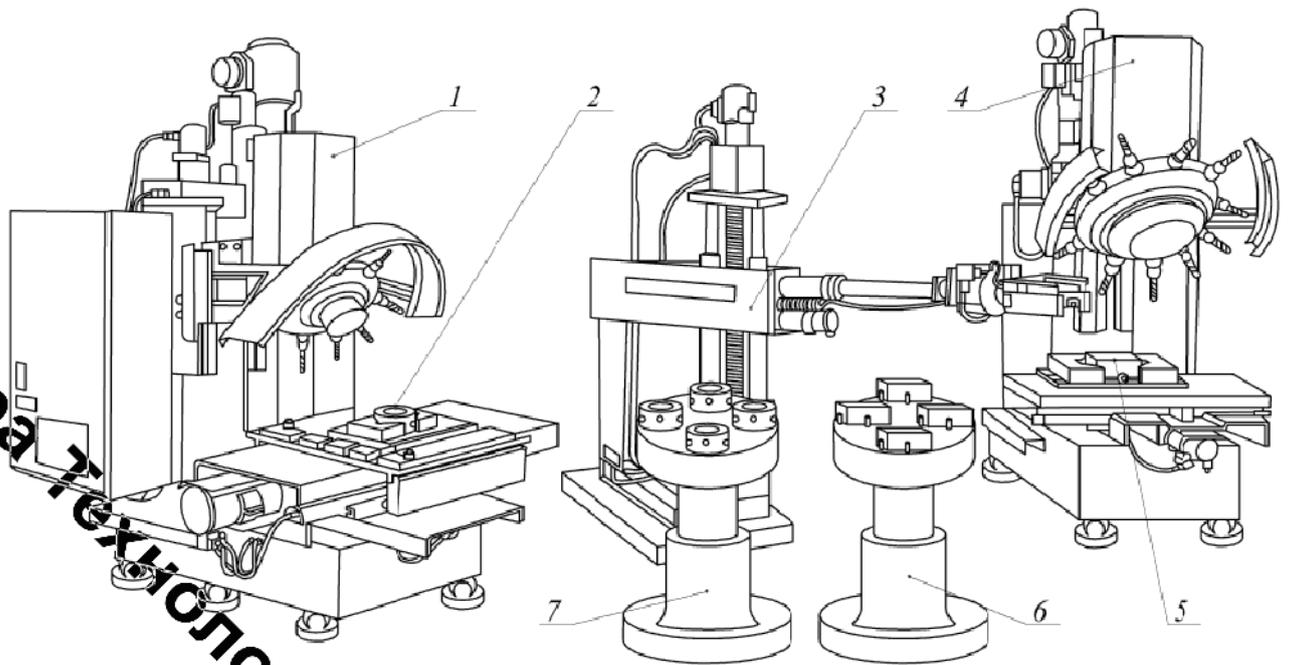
Автоматизований комплекс для фрезерної обробки
